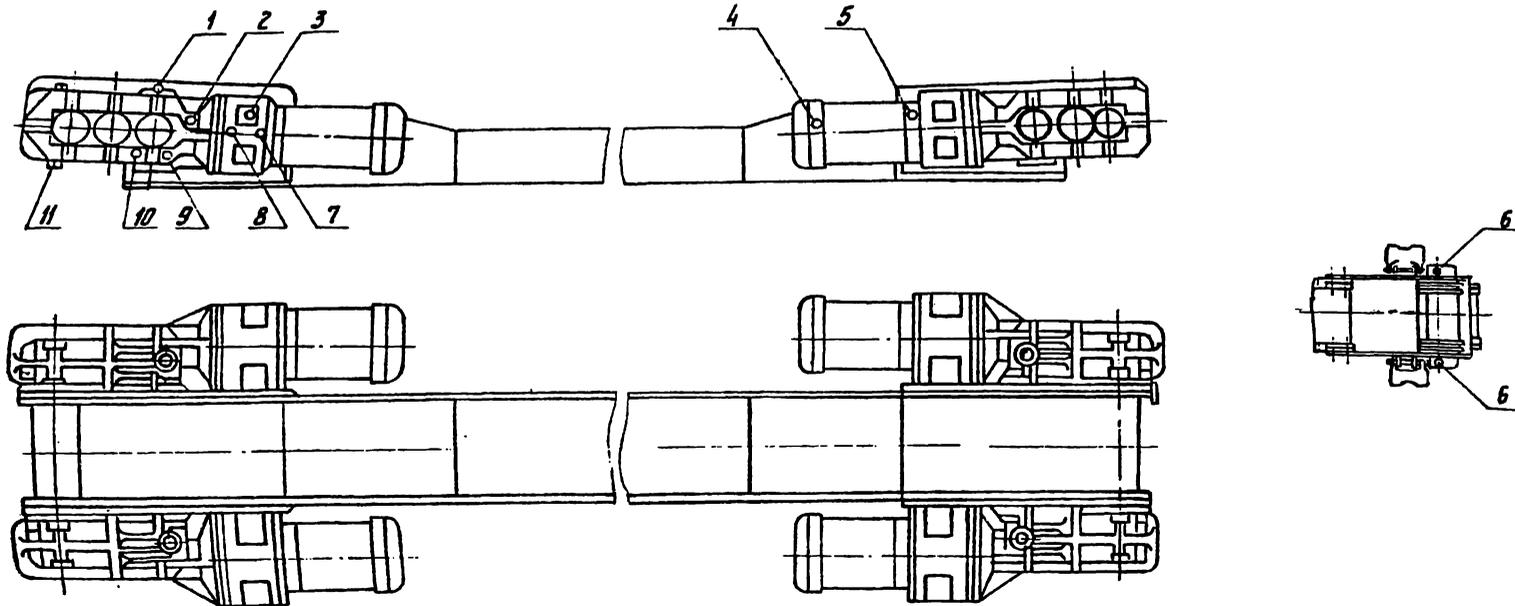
Схема смазки скребкового конвейера с двигателями мощностью 55 кВт
